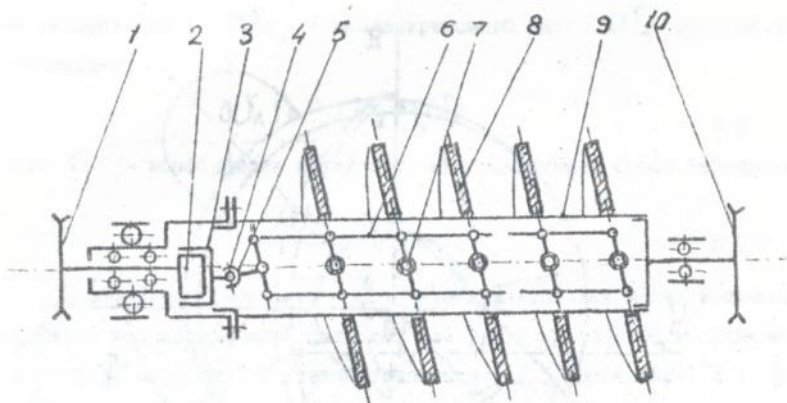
Кинематическая схема дискового барабана с активными дисками: 1 - привод эксцентрикового вала механизма колебания дисков; 2 - эксцентрик; 3 - обойма эксцентрика; 4 - поводок; 5 - вилка; 6 - тяга; 7 - поворотный рычаг; 8 - диск; 9 - трубчатый вал; 10 - привод дискового барабана
